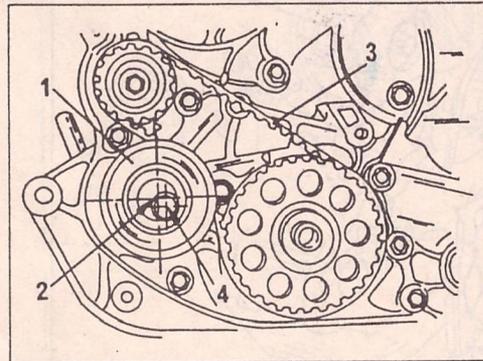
Стрелки указывают на метку колеса масляного насоса и метку корпуса.
